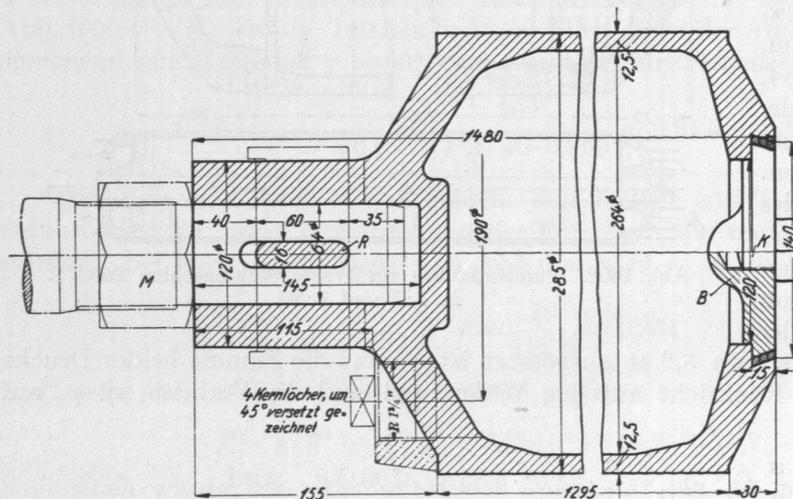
Pumpenkolben zur Wasserwerkmaschine Tafel I. M. 1 : 5.
